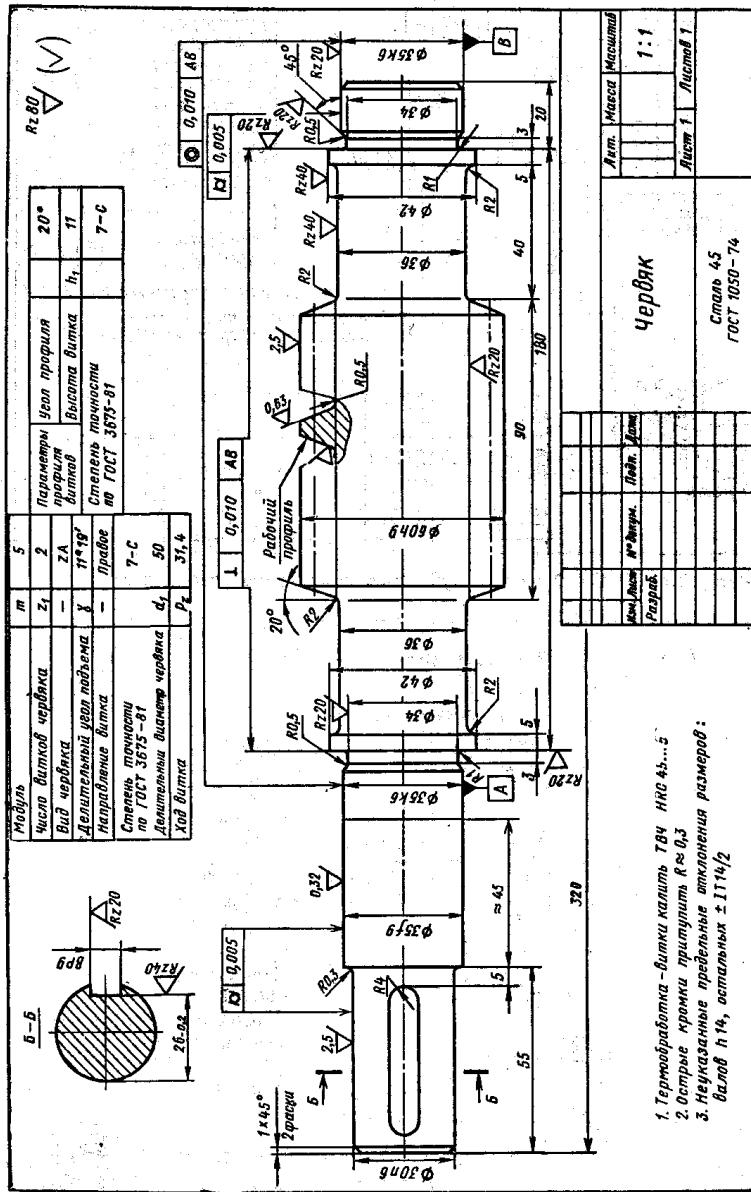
Рабочий чертёж архимедова цилиндрического червяка
